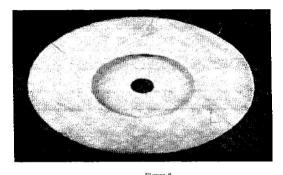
Pieza primaria vista frontal con agujero aspirador y en el centro hoyo de ensamble a la polea del motor.
